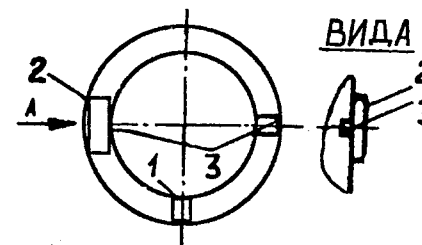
Измерение запилки на привалочной поверхности цилиндра
